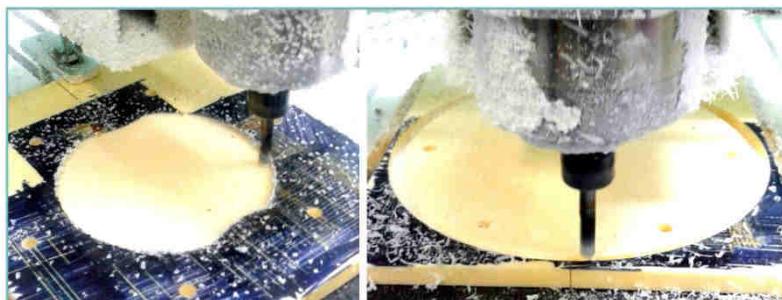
Обработка заготовки из полиуретана LasilCast 2
